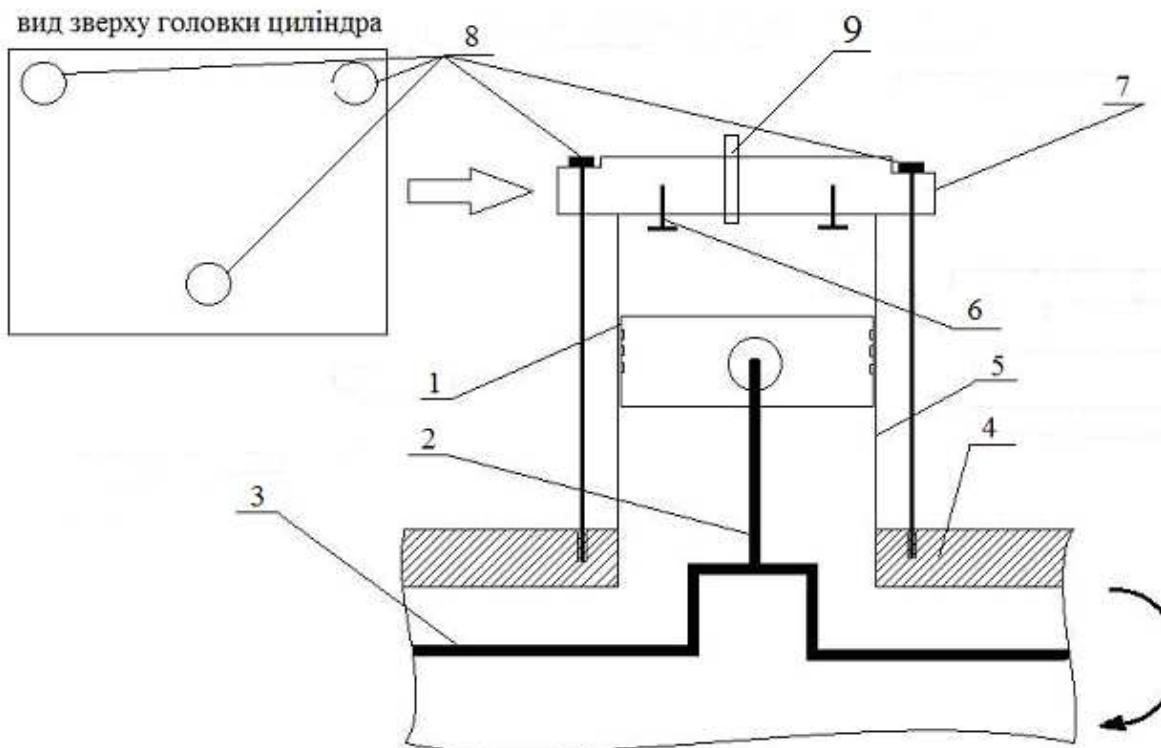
Схема закріплення головки циліндра до картера двигуна: 1 – поршень; 2 – шатун; 3 – колінчастий вал; 4 – блок картера; 5 – гільза циліндра; 6 – впускний та випускний клапани; 7 – головка циліндра; 8 – болти з'єднання головки циліндра та блока; 9 – форсунка
